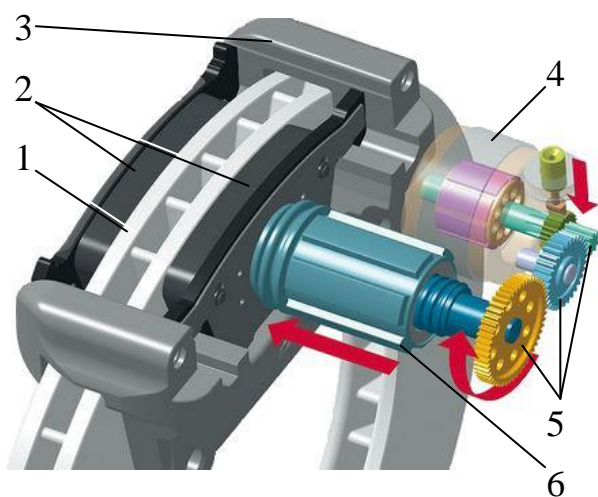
Привод электромеханического стояночного тормоза с цилиндрическим редуктором: 1 – тормозной диск; 2 – тормозные колодки; 3 – суппорт тормозного механизма; 4 – электродвигатель; 5 – шестерни редуктора; 6 – винтовая пара
